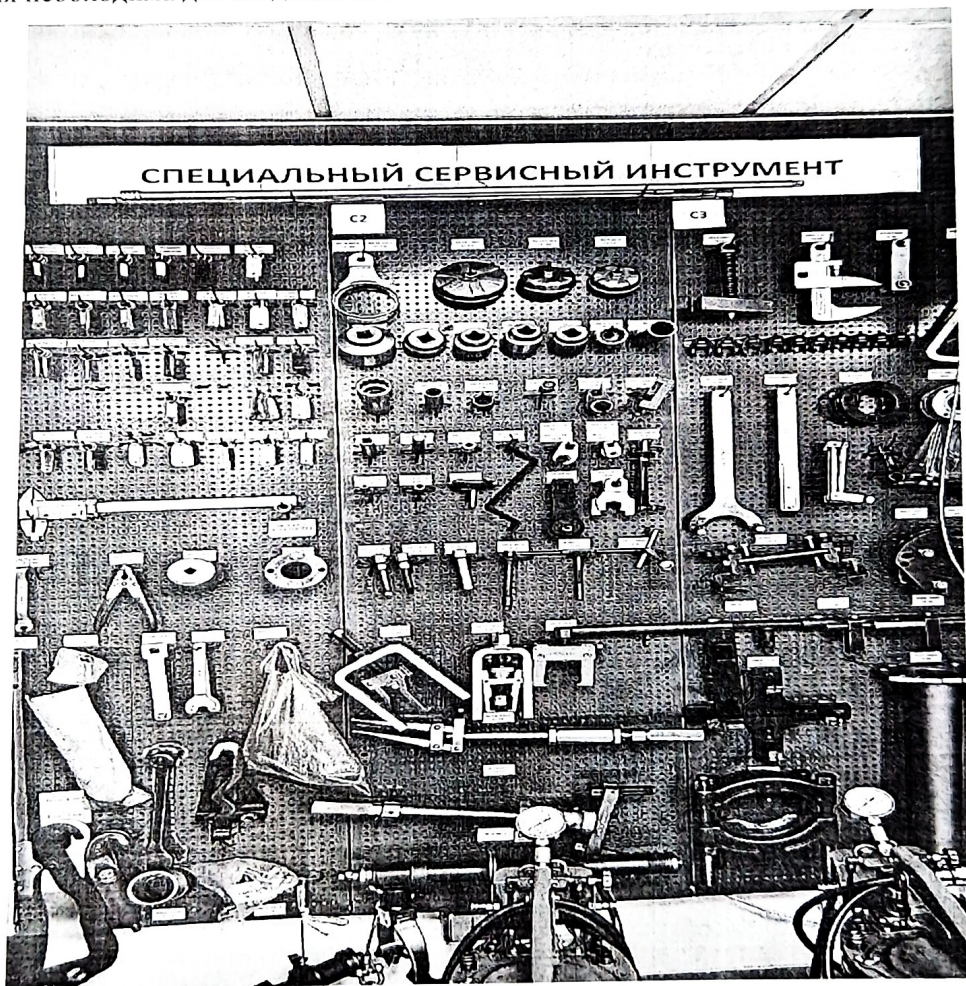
SST (Special Service Tool) — специальный сервисный инструмент
